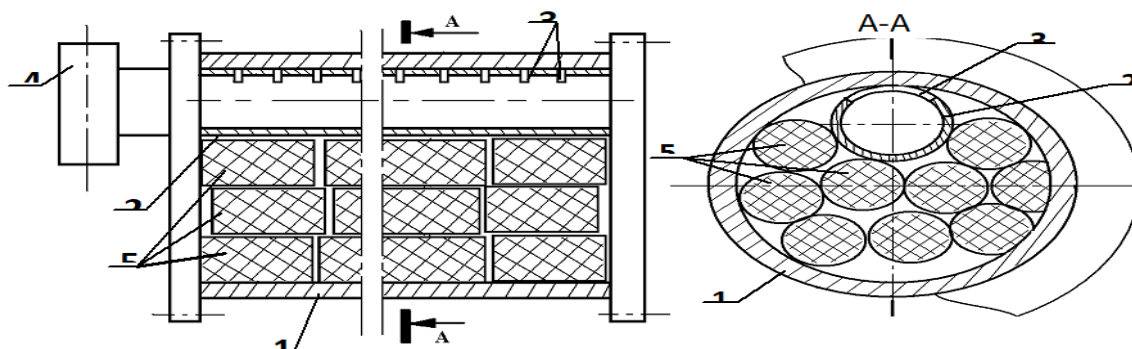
Схема реактора с цилиндрическими сетчатыми капсулами октоаммиаката соли сорбента в цилиндрическом реакторе: 1 – корпус цилиндрический; 2 – внутренняя перфорированная трубка; 3 – дугообразные щелевые отверстия; 4 – хладопровод; 5 – капсулы аммиаката соли
